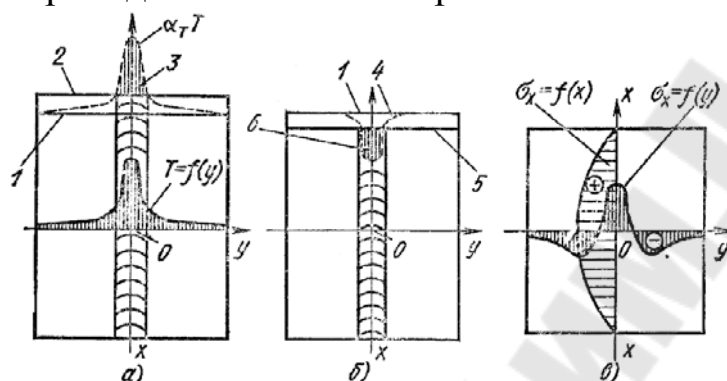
Схема напряженного состояния сварного шва
